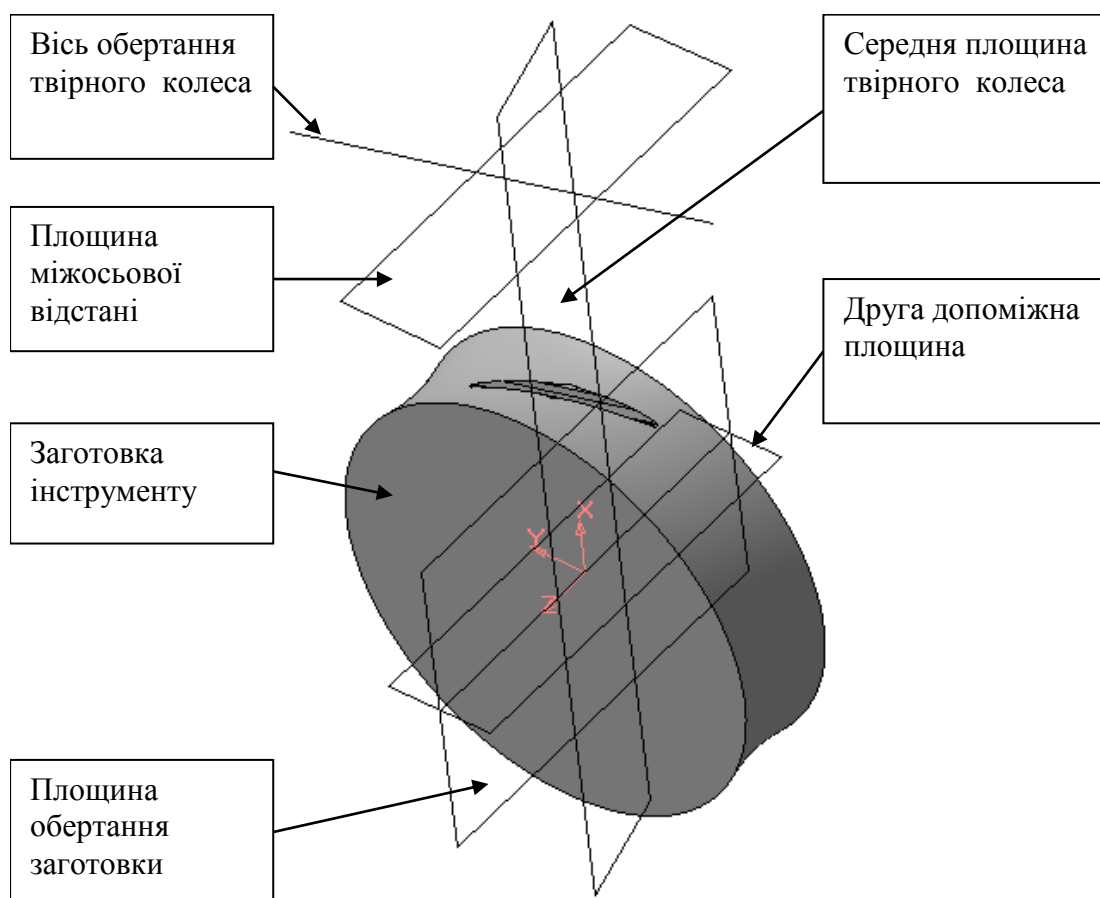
Заготовка інструменту з допоміжними побудовами
